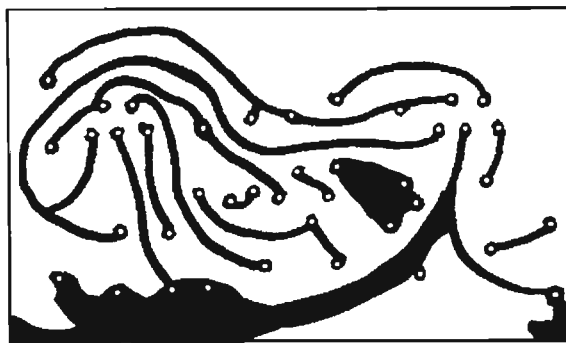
C – Aspecto do verso da placa, local em que se faz a soldagem dos componentes, em escala 1:1.
